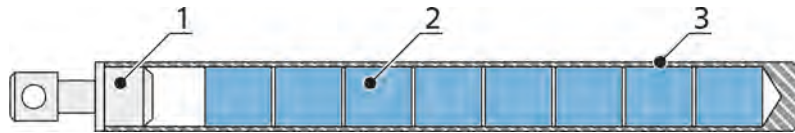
Эскиз конструкции ампулы со стартовым материалом: 1 — корпус; 2 — медные таблетки с изотопами; 3 — пробка
